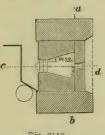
Grundriß nach gh. Einfacher Schachtofen.
